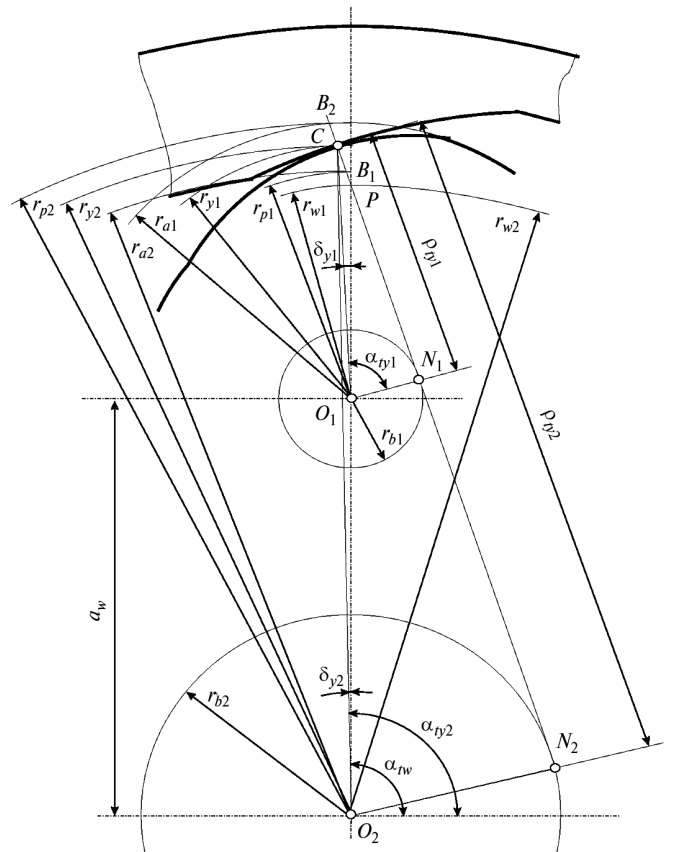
Схема внутреннего зацепления цилиндрической передачи
